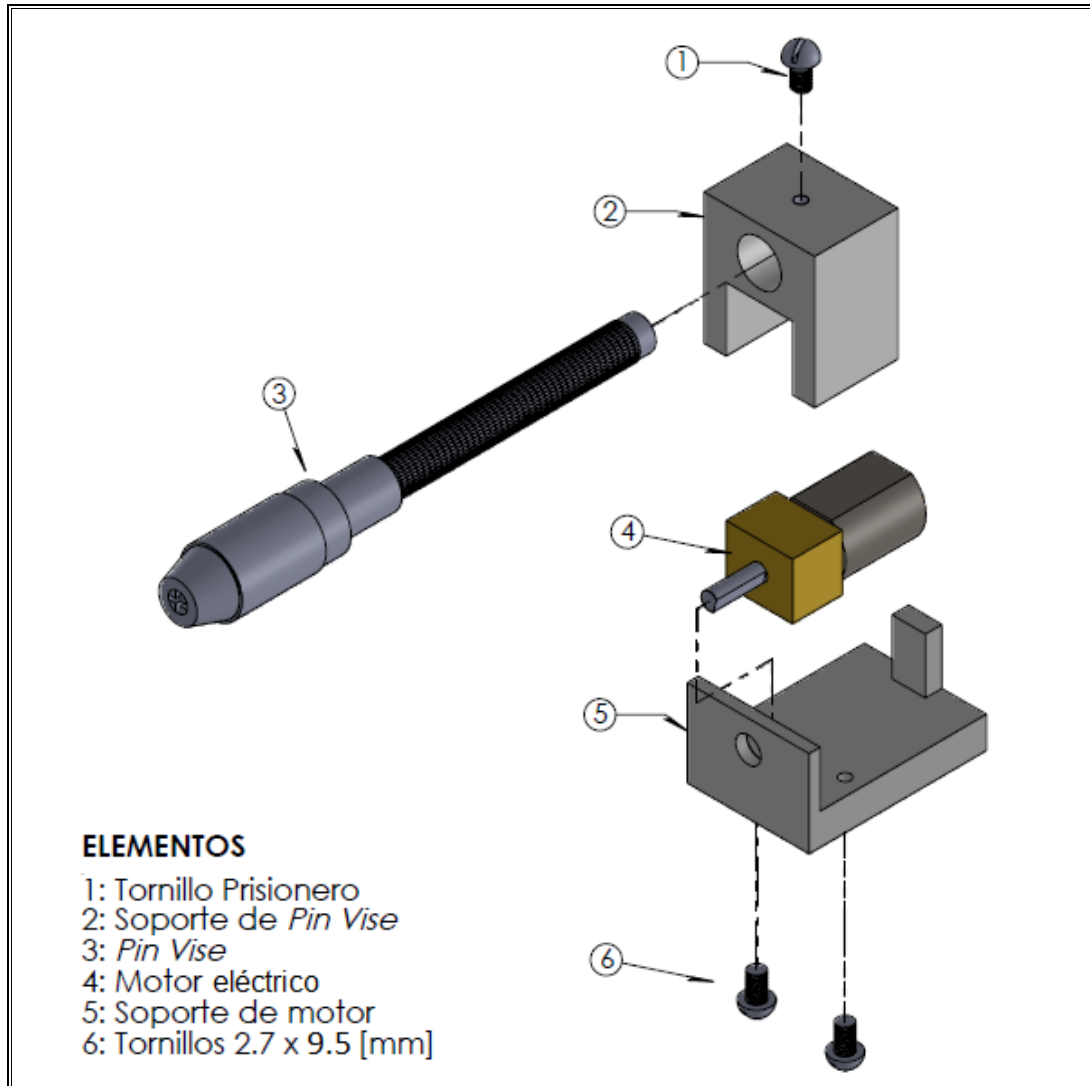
Dibujo del diseño original del subensamble: Soporte de motor – Soporte de *Pin Vise* – Motor. Se aprecia el Motor eléctrico con el Reductor de velocidad resaltado en color dorado.
